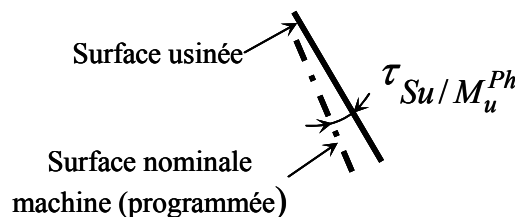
Écart entre la surface usinée et la surface nominale machine
